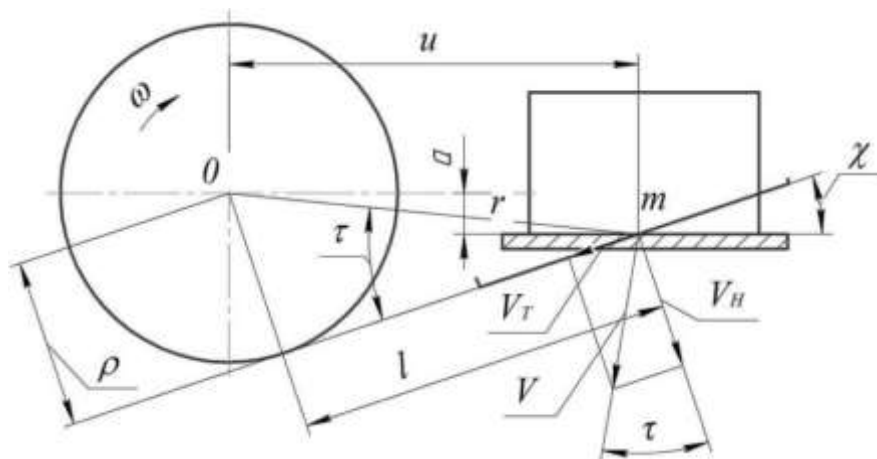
Схема режущего аппарата с прямолинейными ножами
